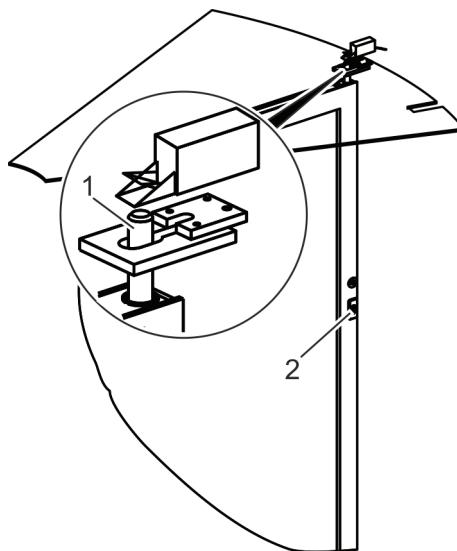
Разблокировка блокировочного устройства со штангой (опция)
